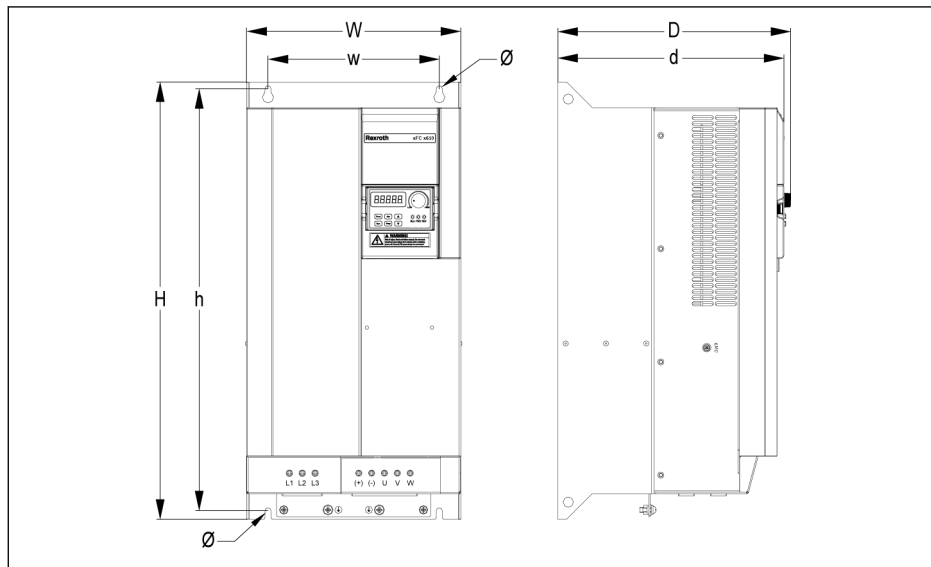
Размерный чертёж EFC 5610 30K0...37K0
